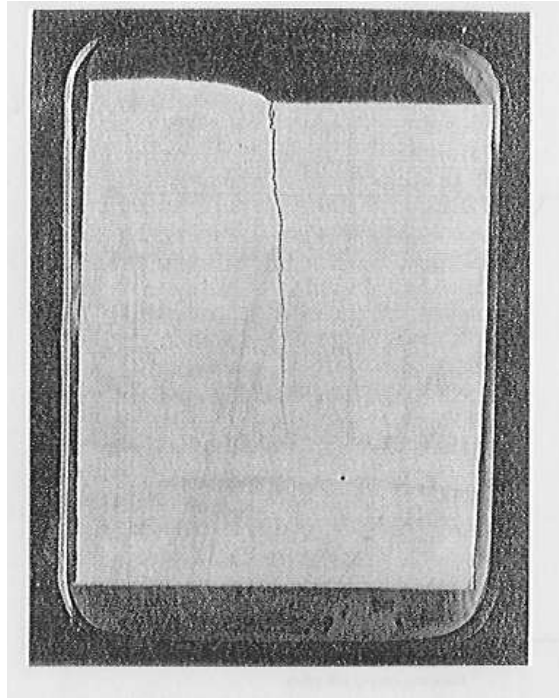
Muestra la superficie longitudinal de una soldadura que se agrieta en el reinicio del arco.
